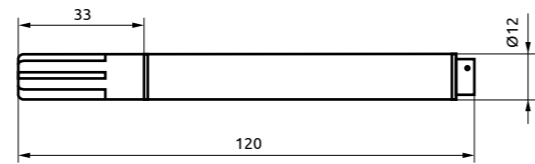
Габаритный размер НТЕ.РF с разъемом
